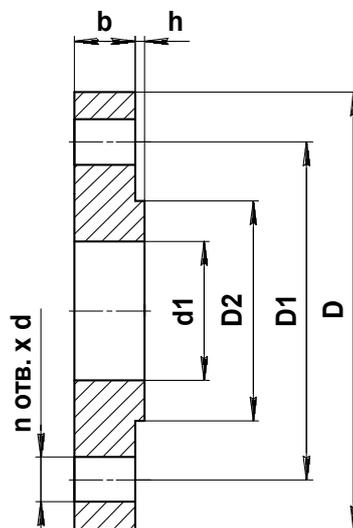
Габаритные и присоединительные размеры ответных фланцев
